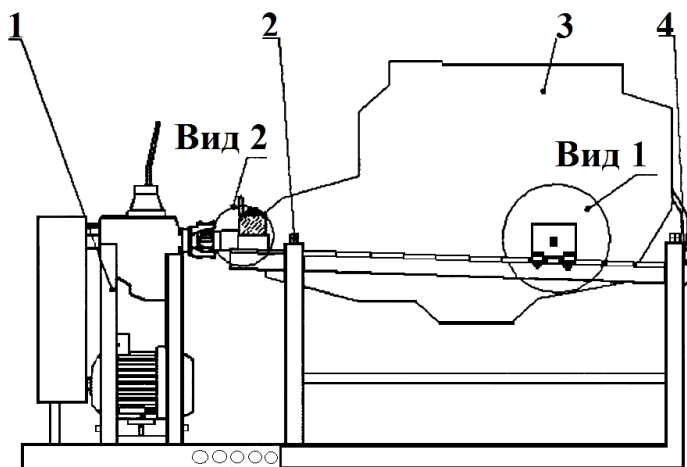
Стенд для обкатки ДВС, вид сбоку
